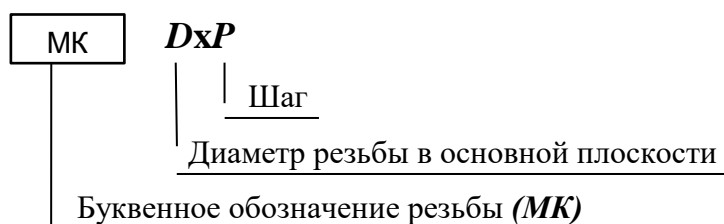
Образец обозначения метрическая конической резьбы.
